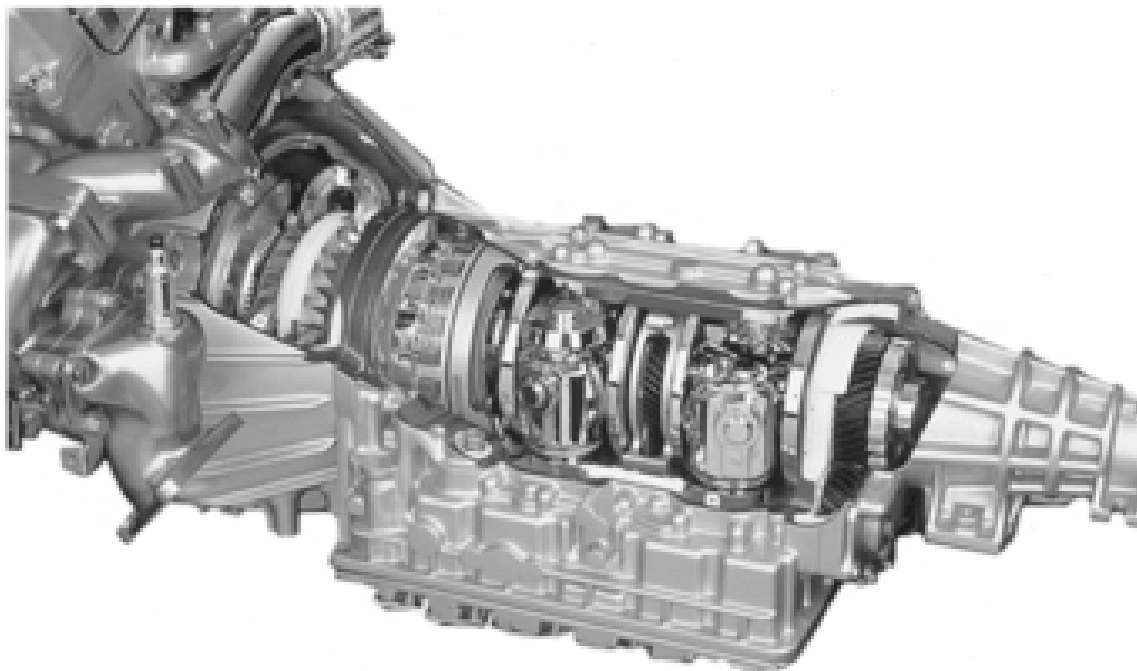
Коробка передач Nissan Extroid з тороїдальним варіатором [8]
